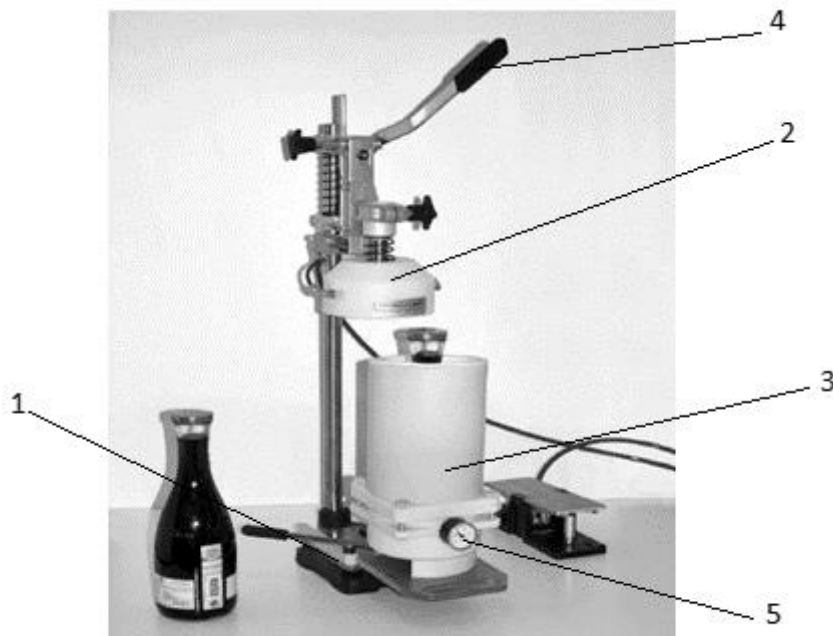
Загальний вигляд пристрою закупорювання УУ-5
